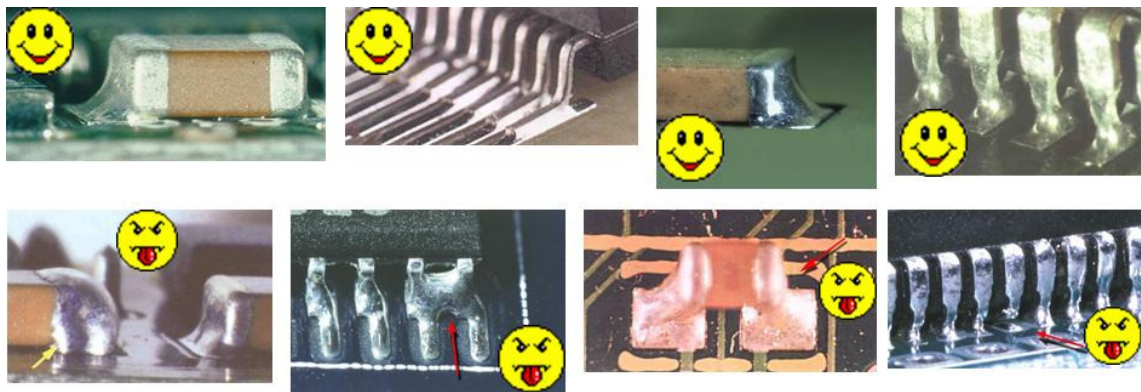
Exemplos de boas e más soldaduras
